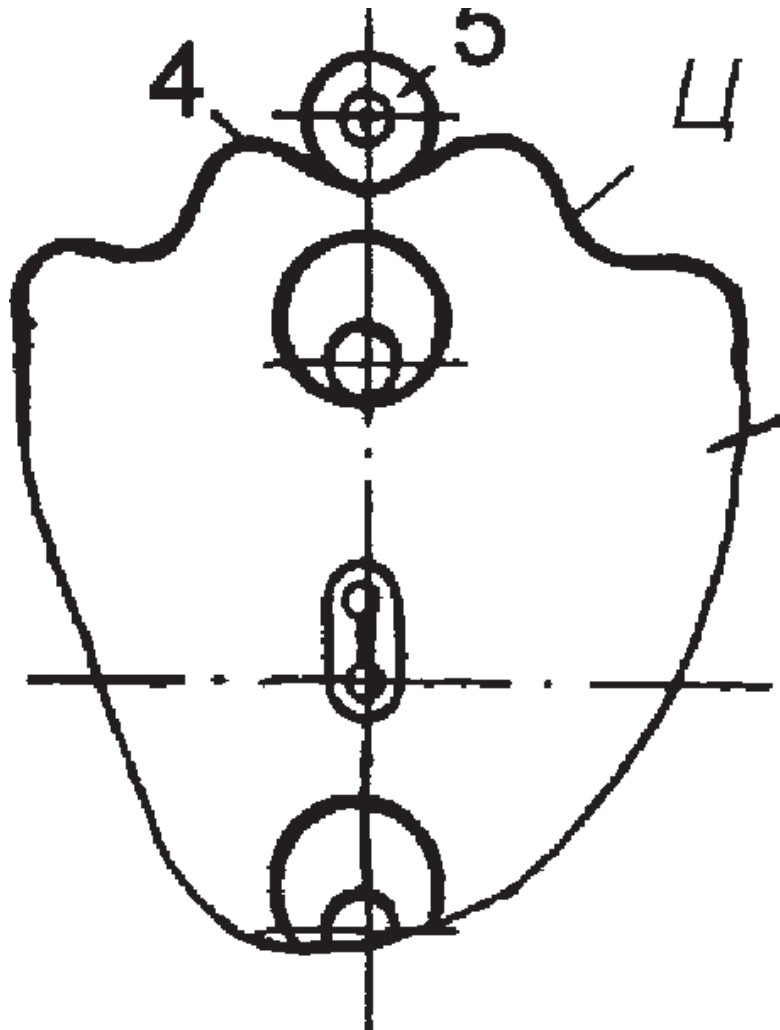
Планетарно-цевочный редуктор схемы *K-H-V
